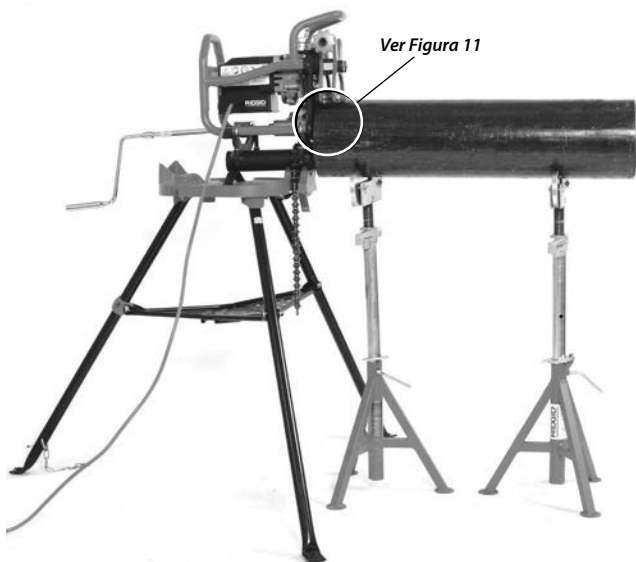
Biselador Fixo, Tubo Comprido, Vários Suportes de Tubo
